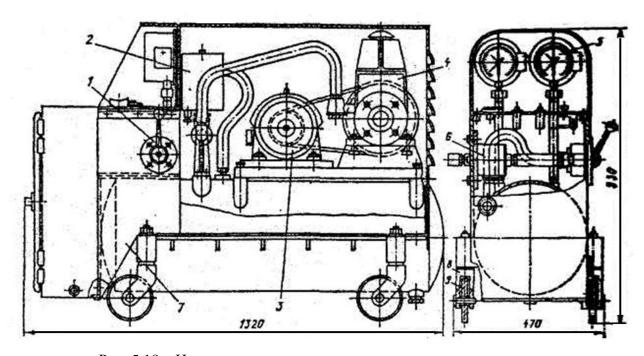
Цеховая портативная установка для создания вакуума
